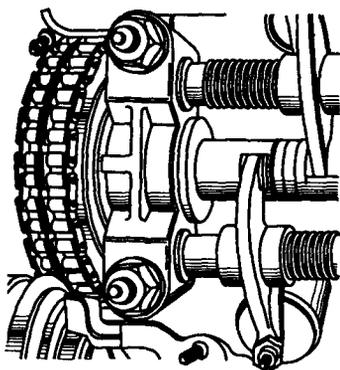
Положение распределительного вала на головке цилиндров двигателя перед установкой головки на блок
